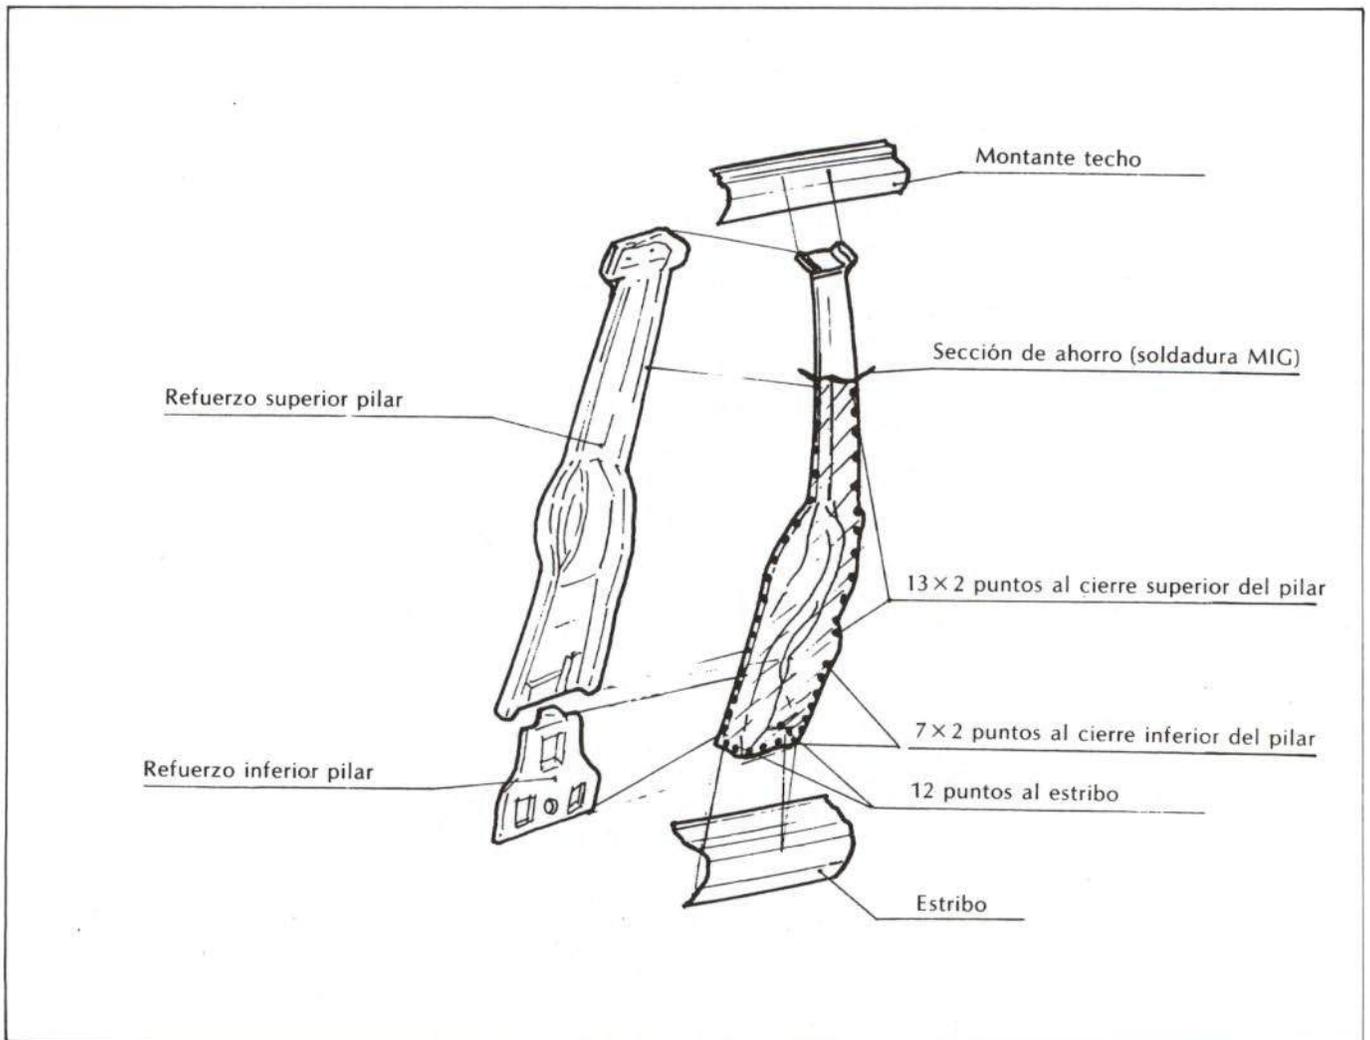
Fijación del pilar central a carrocería. Sección de ahorro.
